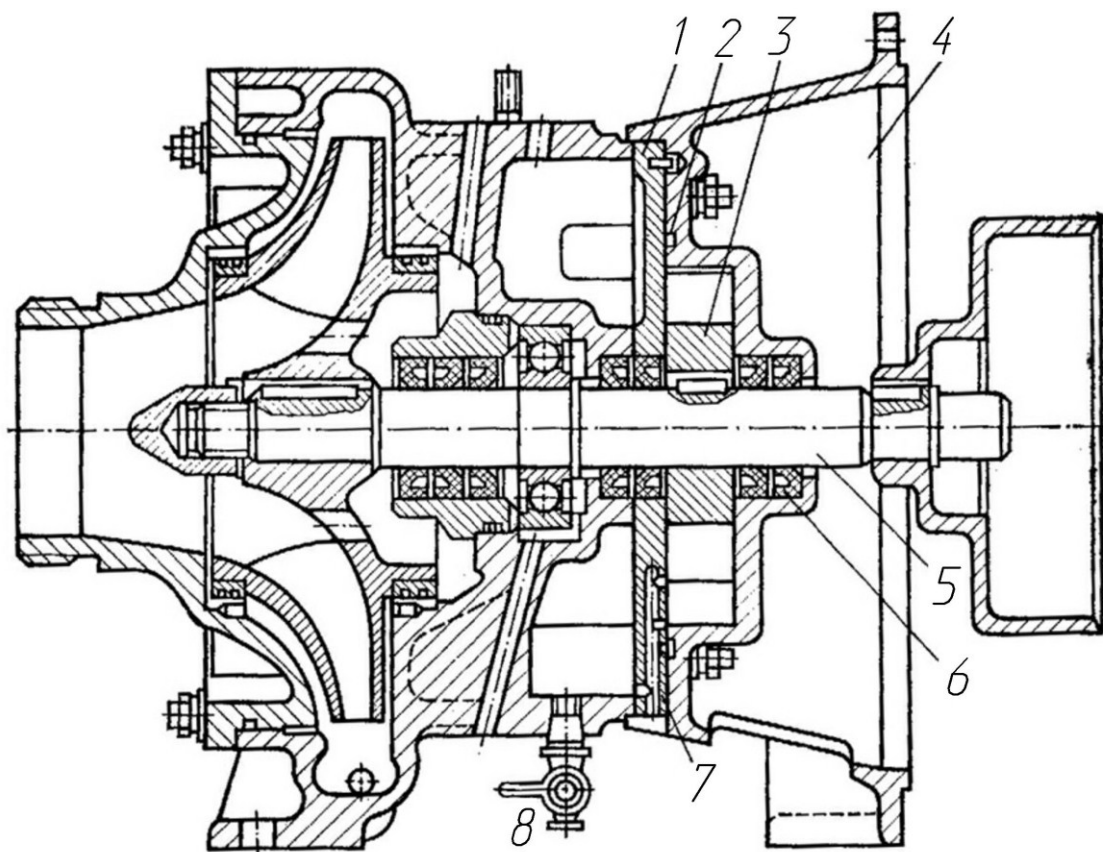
Насос центробежный самовсасывающий НЦС-15: 1-диафрагма; 2-уплотнительное кольцо; 3 - рабочее колесо водокольцевого насоса; 4 - корпус; 5-вал; 6 - сальники; 7 - прокладки; 8 – краник.
